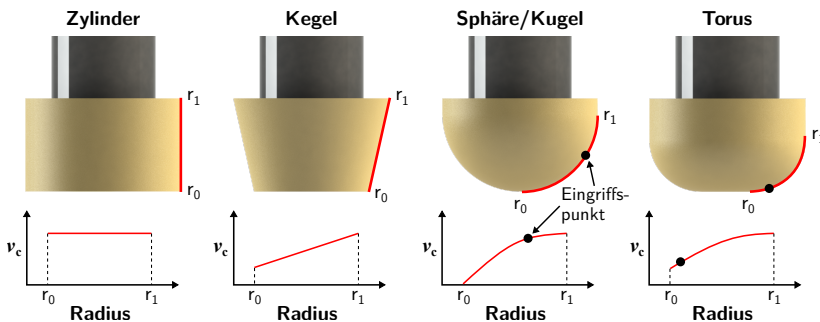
Verwendete Werkzeuggrundformen für die Bearbeitung der beschichteten Tiefziehwerkzeuge und deren Schnittgeschwindigkeitsprofile entlang der möglichen Eingriffsbereiche.
